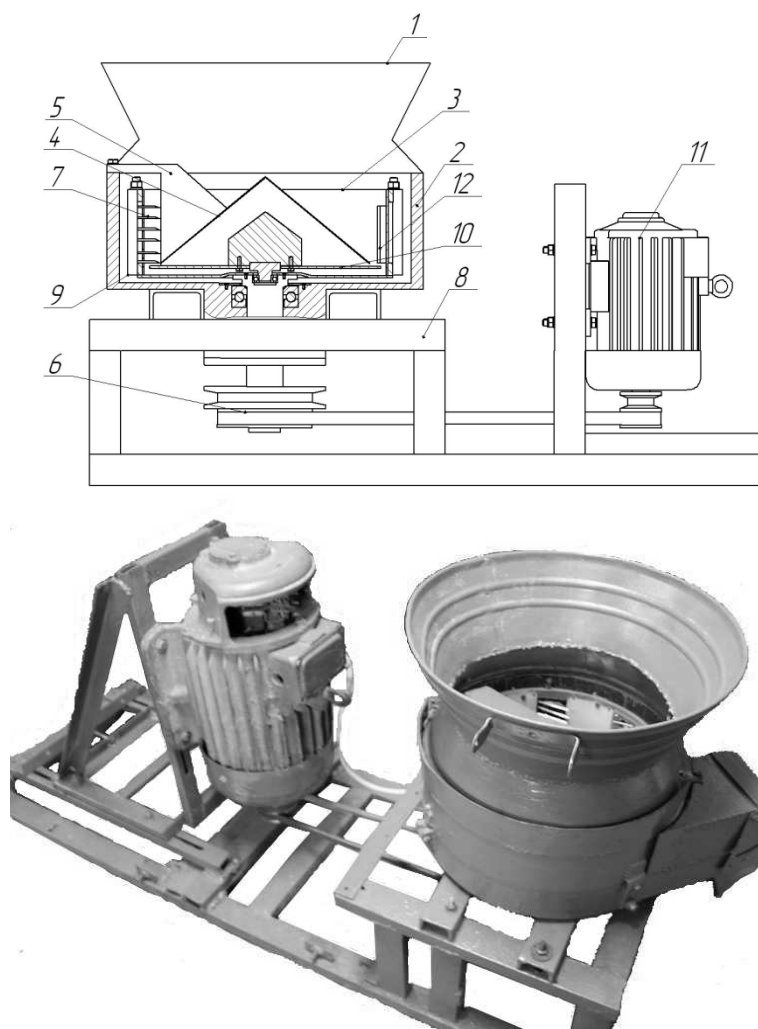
Схема и общий вид измельчителя: 1 – загрузочное окно; 2 – корпус; 3 – ротор; 4 – направляющий конус; 5 – противорежущая пластина; 6 – клиноременная передача; 7 – горизонтальные ножи; 8 – рама; 9 – выгрузные лопатки; 10 – основание; 11 – электродвигатель мощностью 3,5 кВт; 12 – вертикальные ножи
